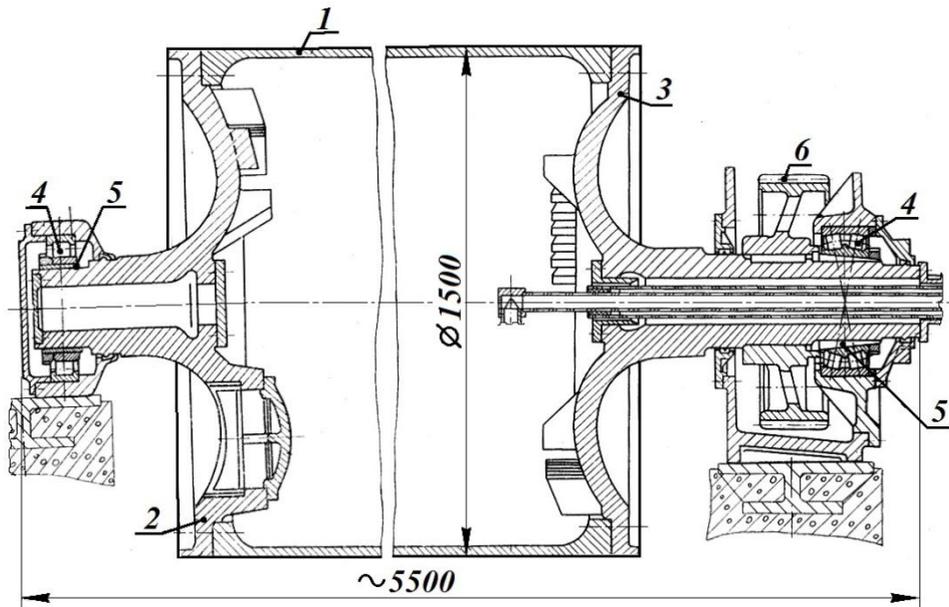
Сушильный цилиндр: 1 – цилиндр; 2 – крышка-цапфа лицевой стороны; 3 – крышка-цапфа приводной стороны; 4 – подшипник качения; 5 – разжимная втулка; 6 – шестерня
